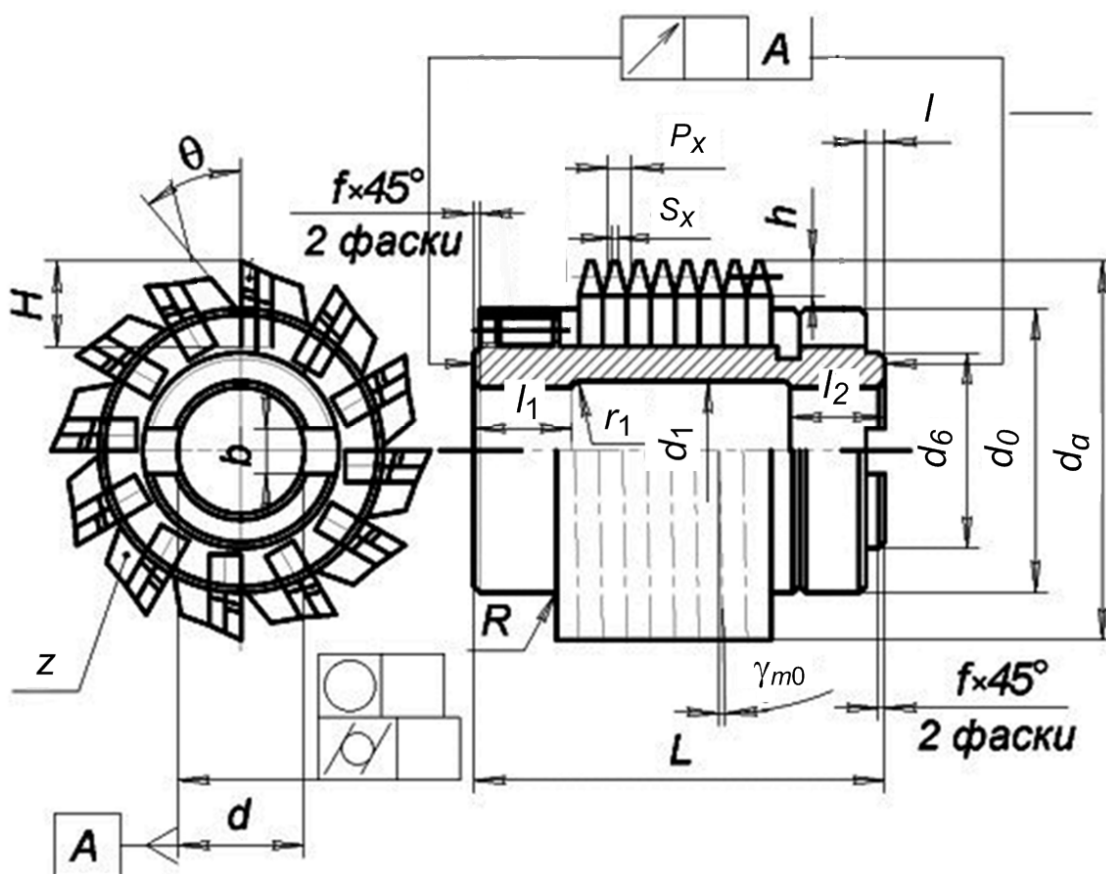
Збірна твердосплавна черв'ячна зуборізальна фреза
